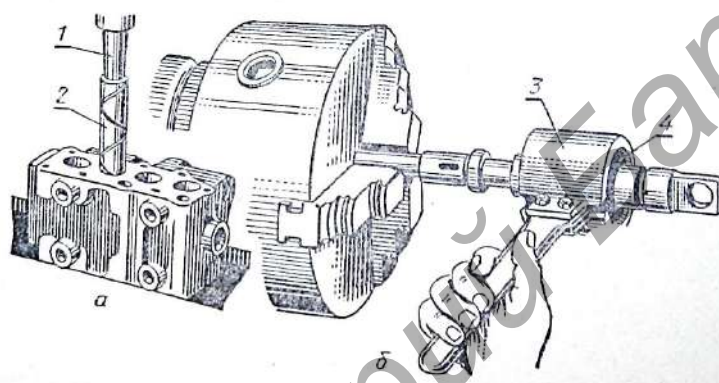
Ремонт золотника и корпуса распределителя:
